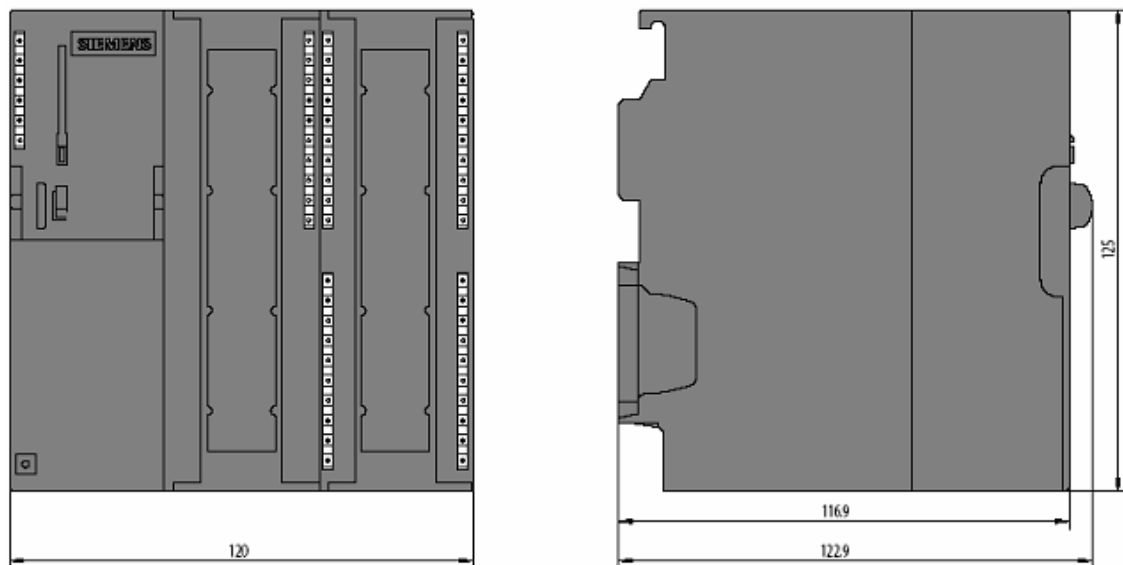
Dimensiones técnicas de la CPU 314C-2DP.
